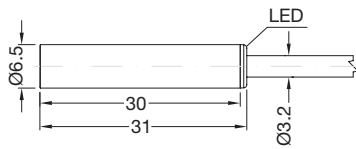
Kurze Ausführung, bündiger Einbau, Kabel
